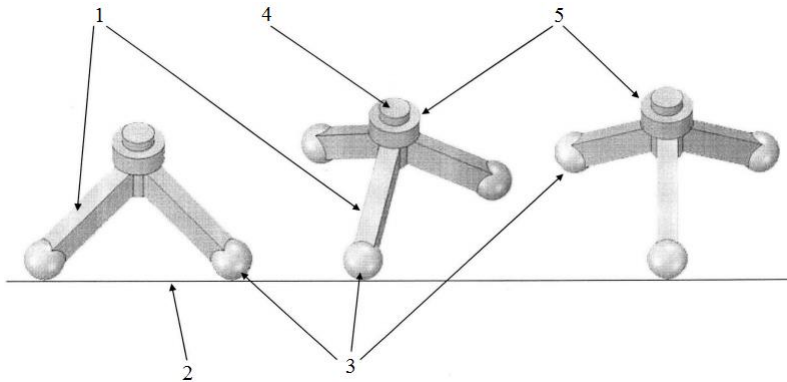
Колісно-кроковий рушій в різних положеннях опор 1 відносно опорної поверхні 2 (вид збоку): 3 – сферична п'ята; 4 – загальний вал; 5 – маточина
